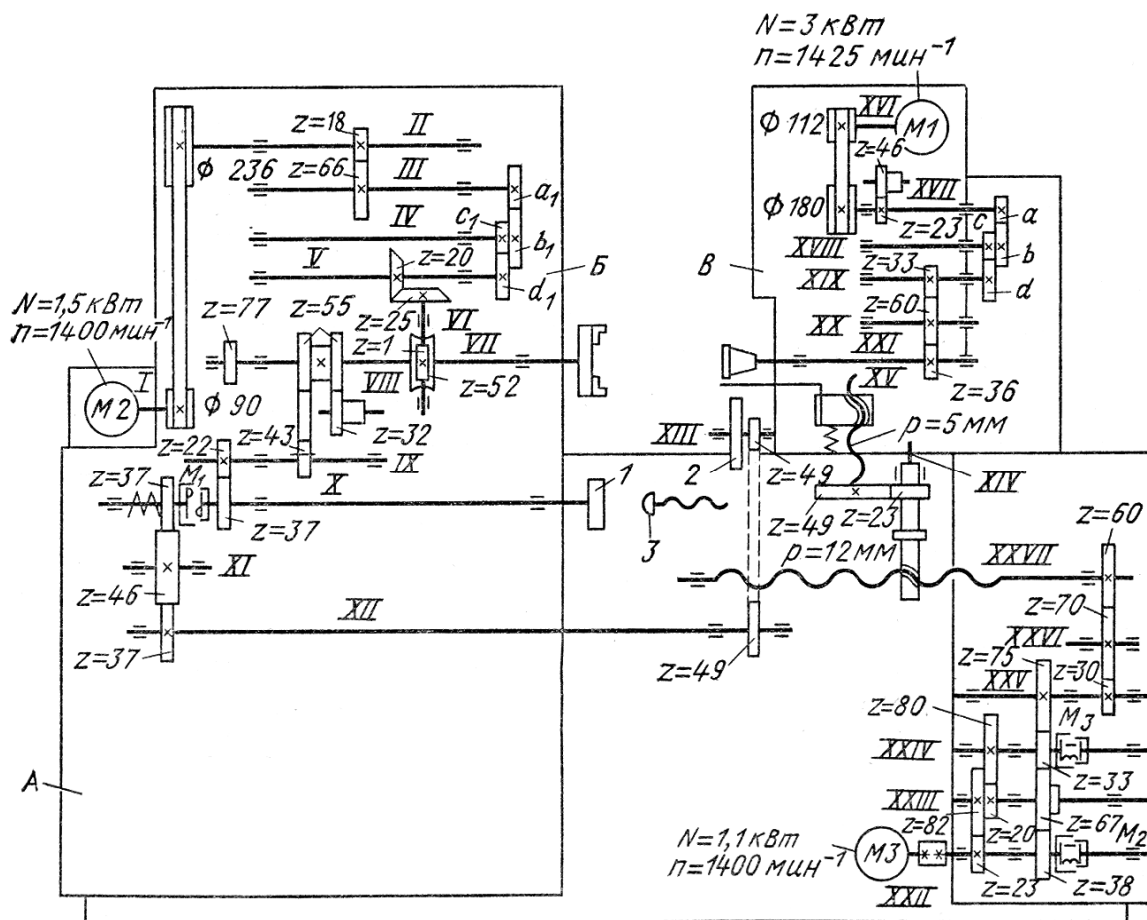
Кинематическая схема резьбофрезерного станка мод. 5Б63
